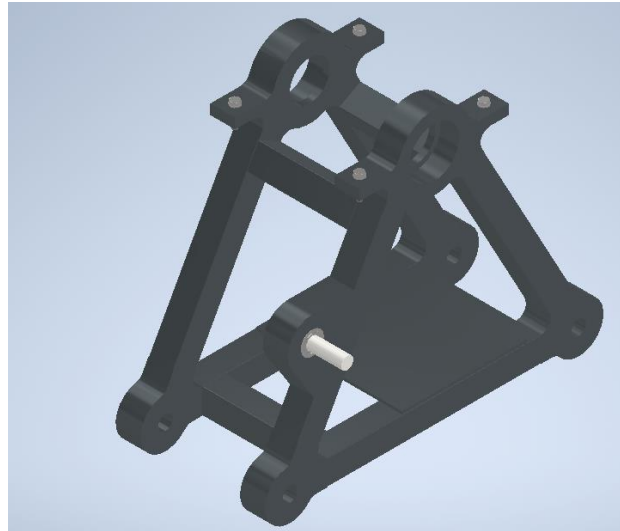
Modelo CAD do carrinho de deslocamento do braço
